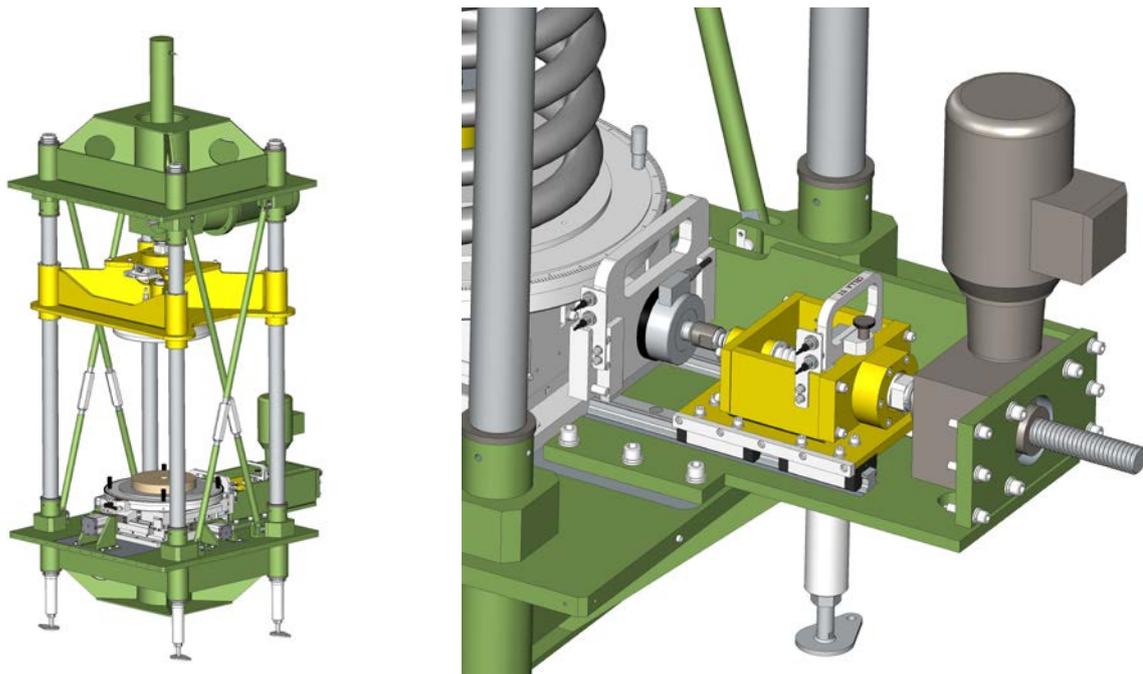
Vista Assieme Pressa Elettromeccanica con Dettaglio Gruppo di Spinta
